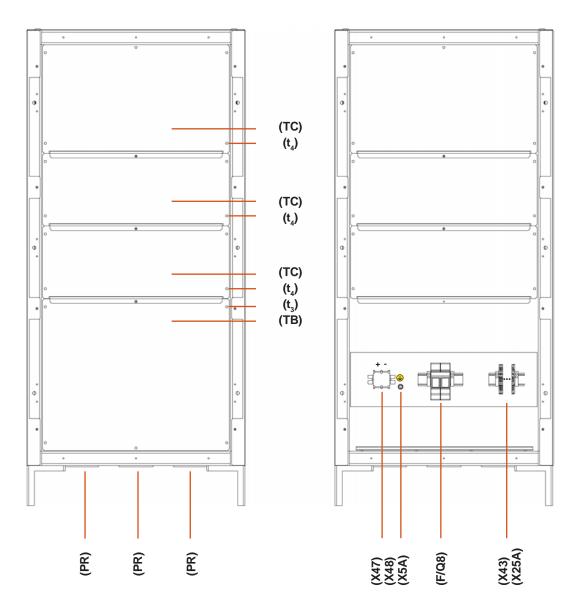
Vista frontal armário de baterias de 605x605x1315 mm.
